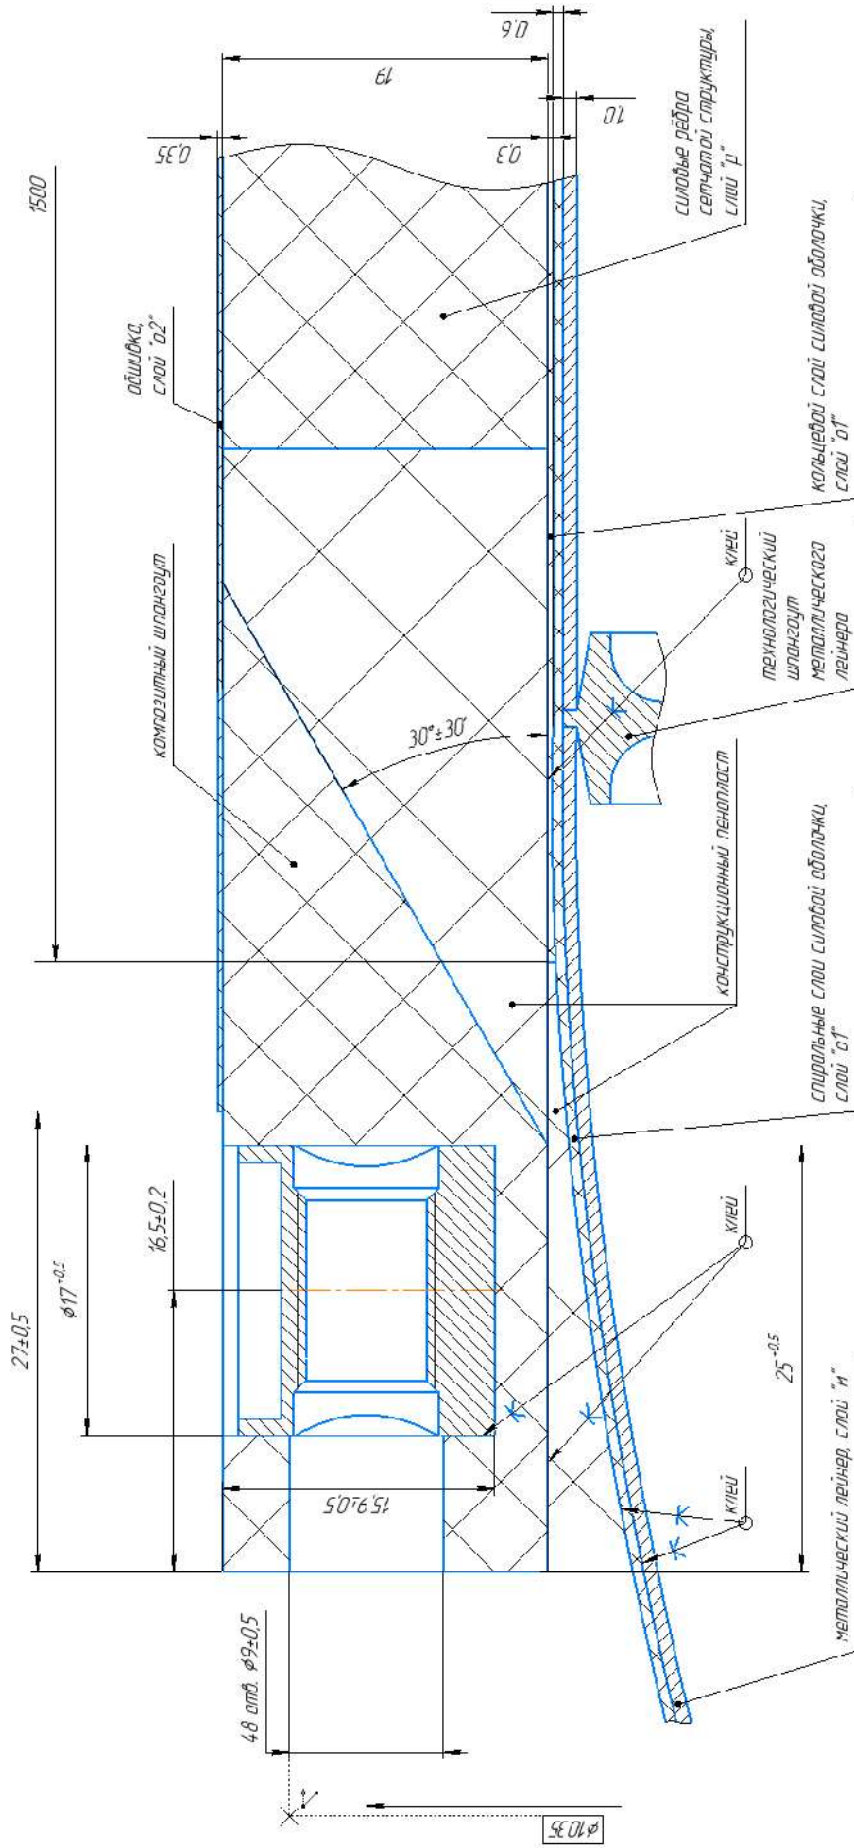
Сечение стенки модели бака с основными размерами
